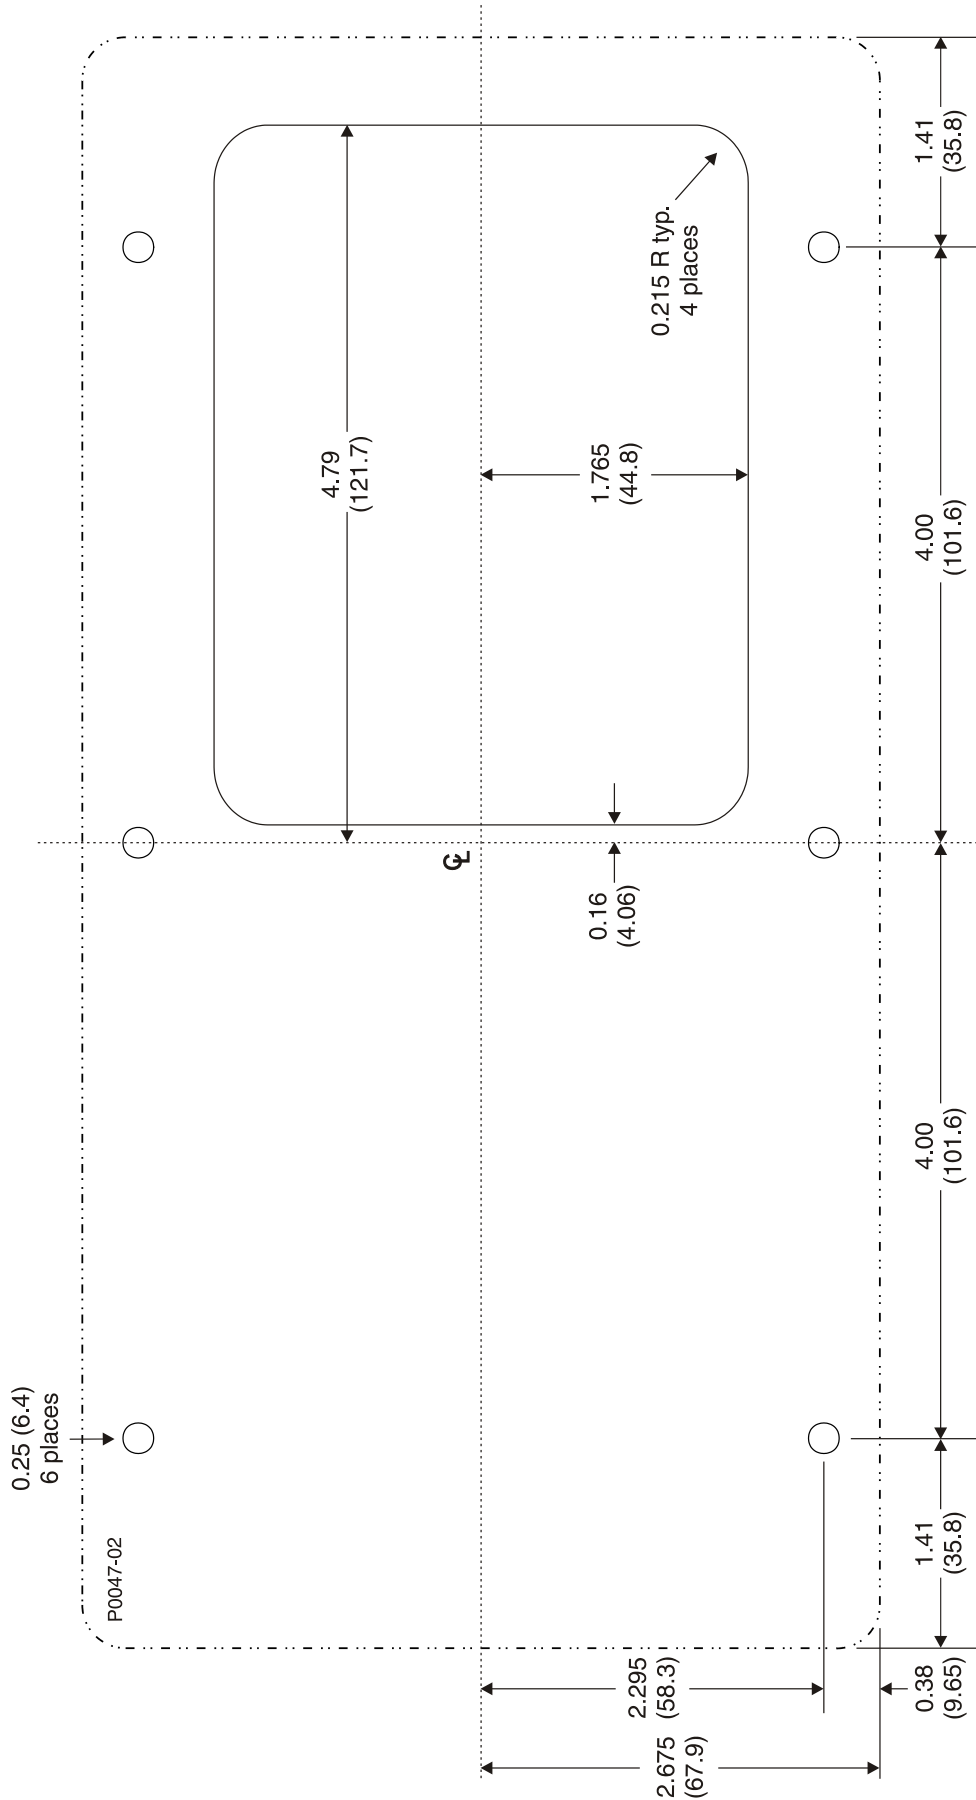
Dimensions de découpes et de perforations, P/N E000-23800
